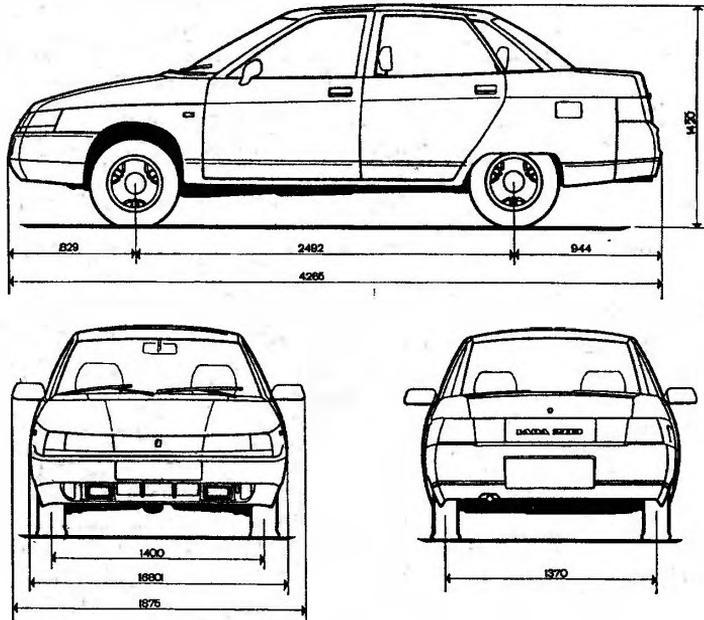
Габаритные размеры автомобиля ВАЗ-2110
